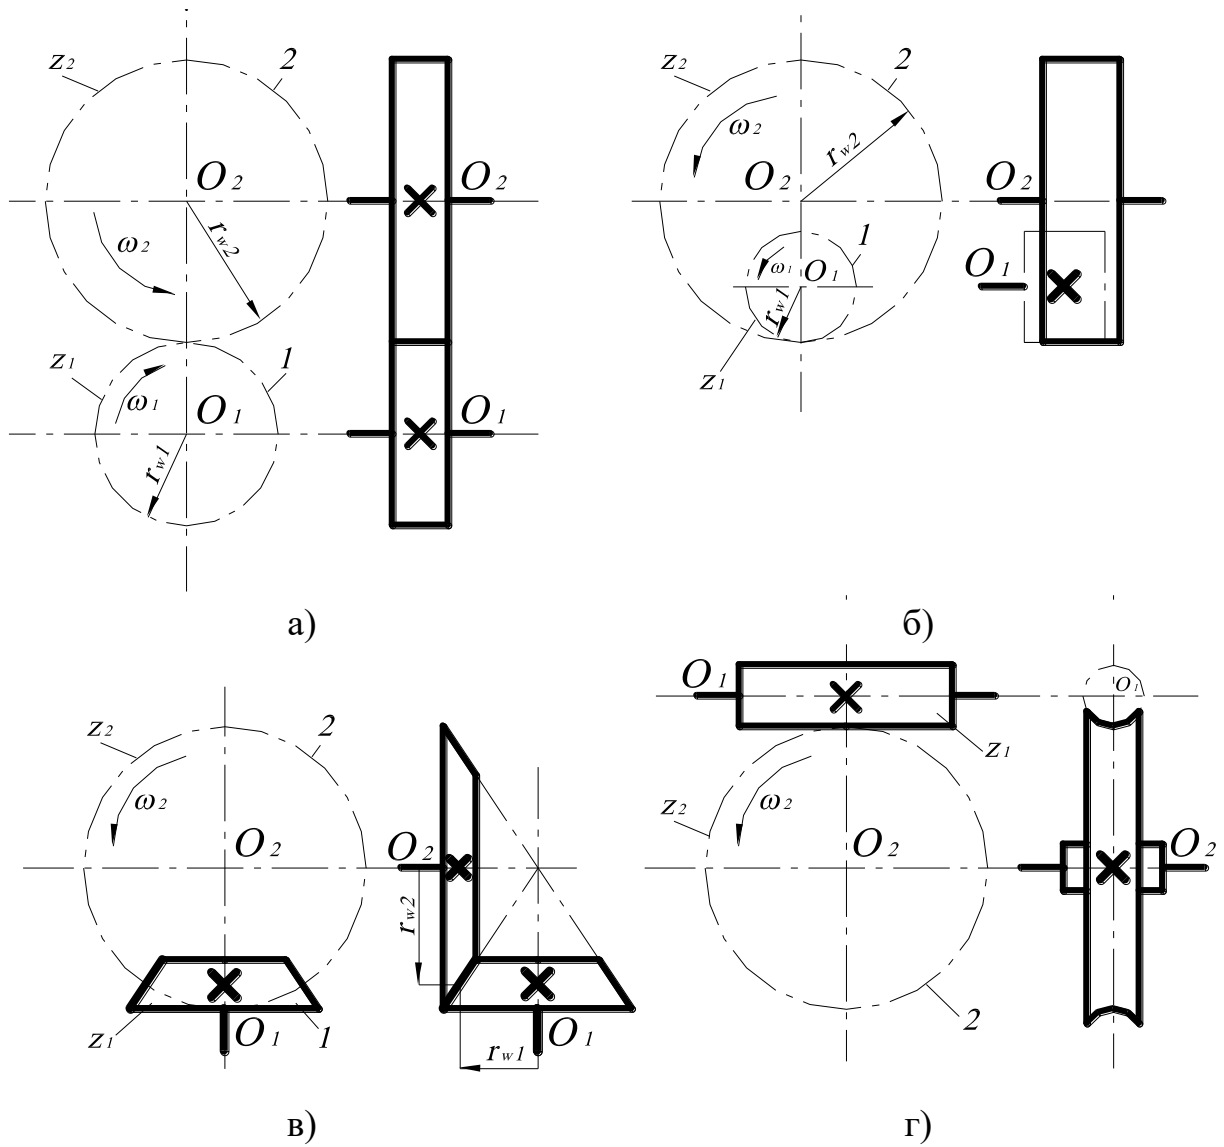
Кінематичні схеми зубчастих передач
